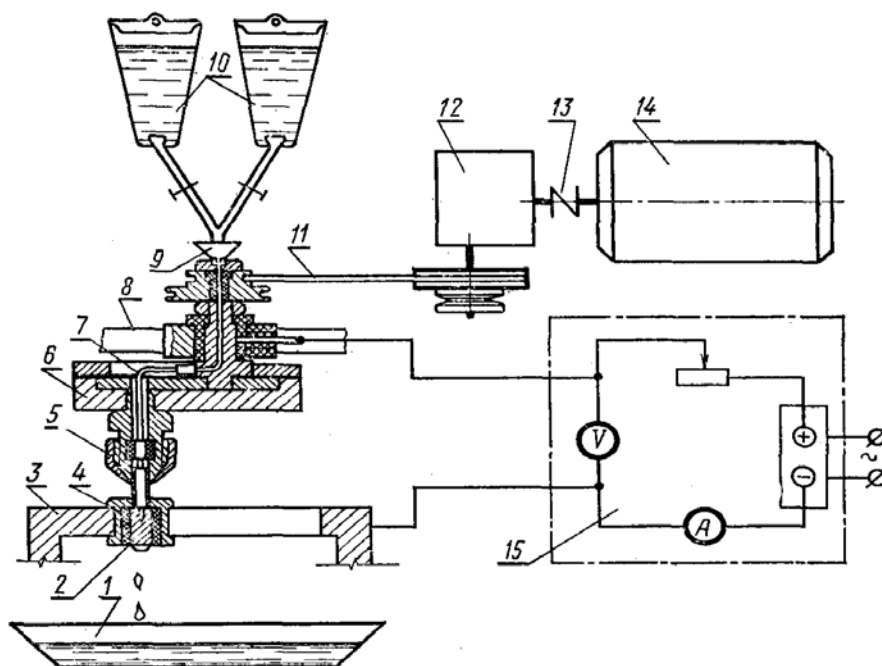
Схема установки для восстановления электронатирием посадочных поверхностей в корпусах коробок передач:
